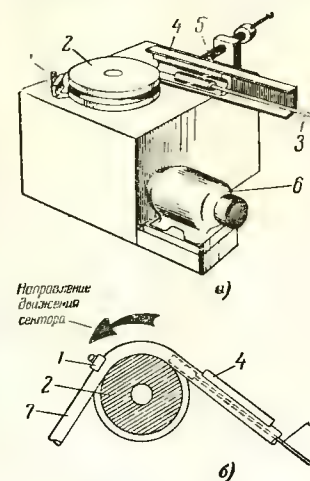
Схема трубогибочного станка и процесс гибки труб.
